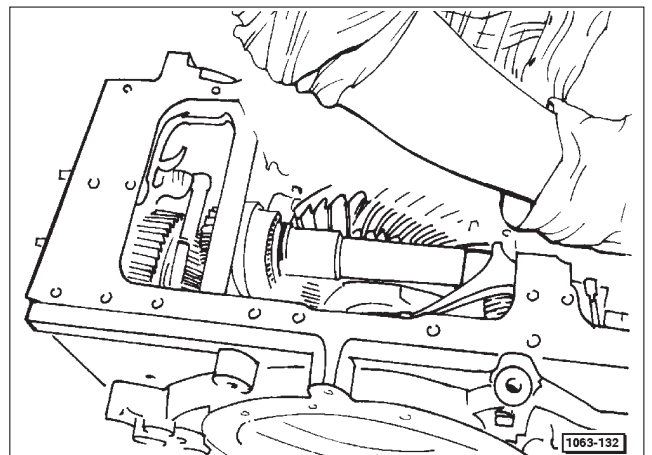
Pousser l'arbre de transmission dans l'ensemble réducteur en ayant soin d'aligner les pièces de manière à positionner correctement l'arbre.
